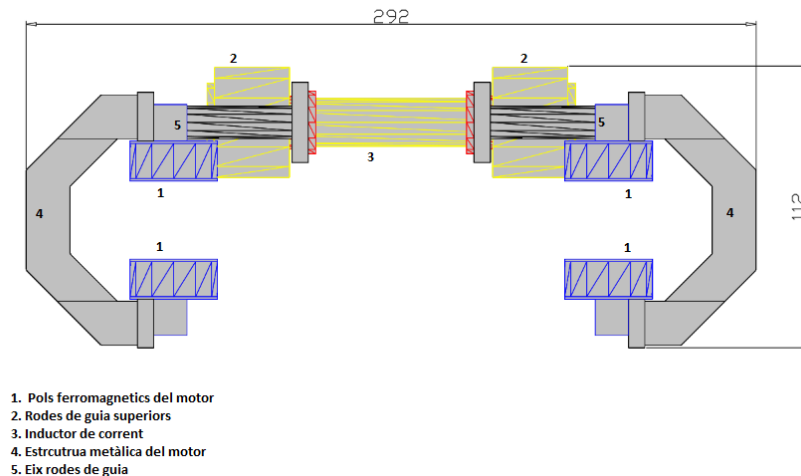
Vista frontal del motor lineal del prototip del TELMAG dimensionat.
